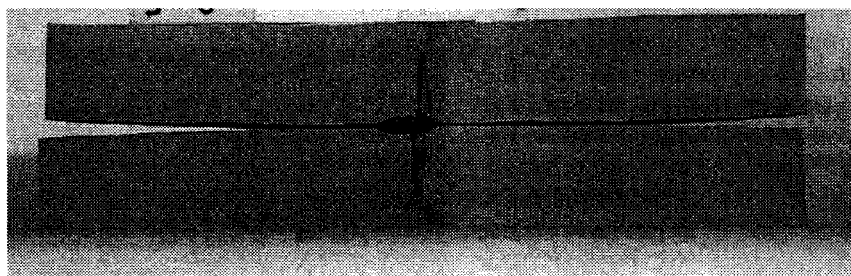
Усадочная пора в продольном изломе проката подшипниковой стали ШХ15СГ
